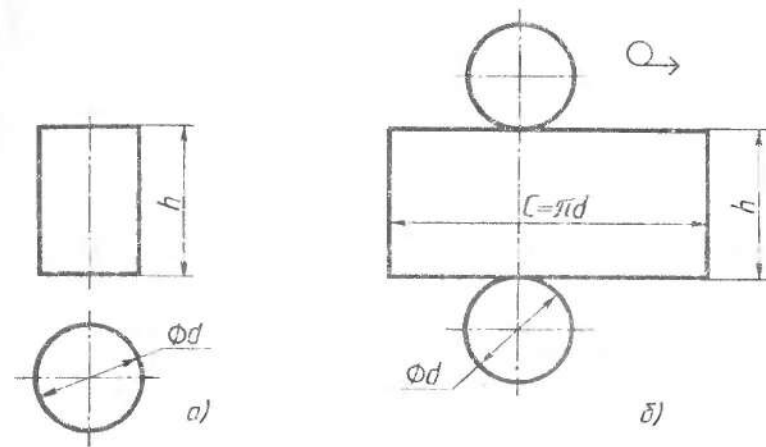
Построение чертежа развертки поверхностей цилиндра: а — два вида; б — развертка поверхностей
